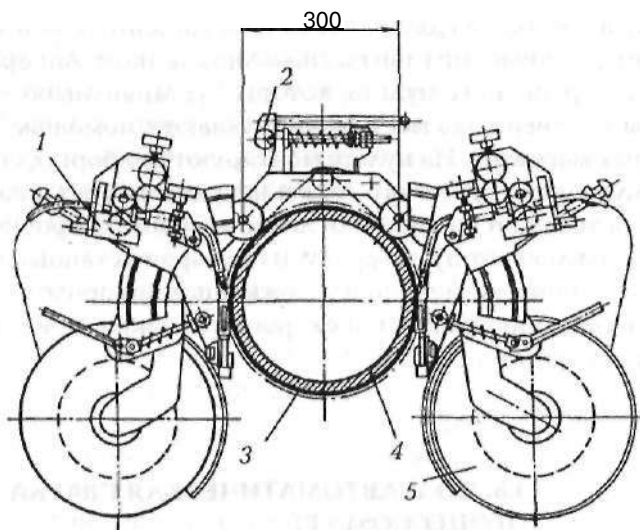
Сварочный аппарат АД-142:
